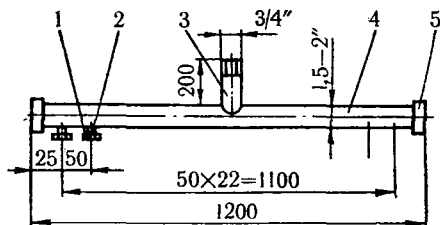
Схема штанги с штуцерами: 1 — гайка-заглушка с отверстием; 2 — трубка; 3 — труба для подвода аммиачной воды; 4 — труба; 5 — муфта-заглушка
